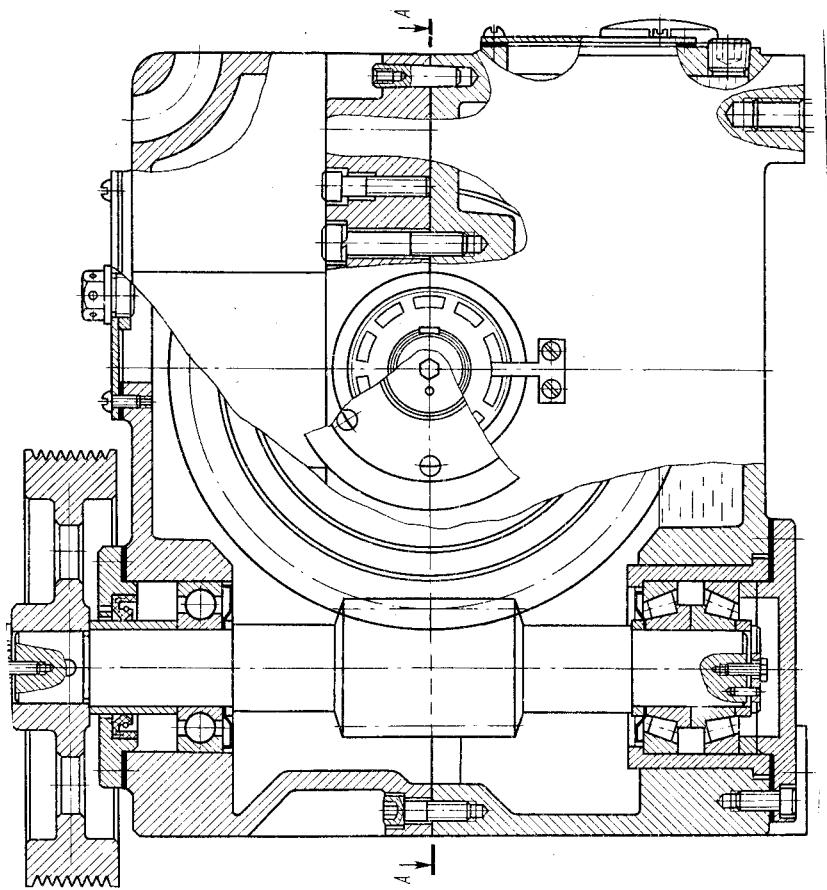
Редуктор червячный одноступенчатый с вертикальным валом червяка
